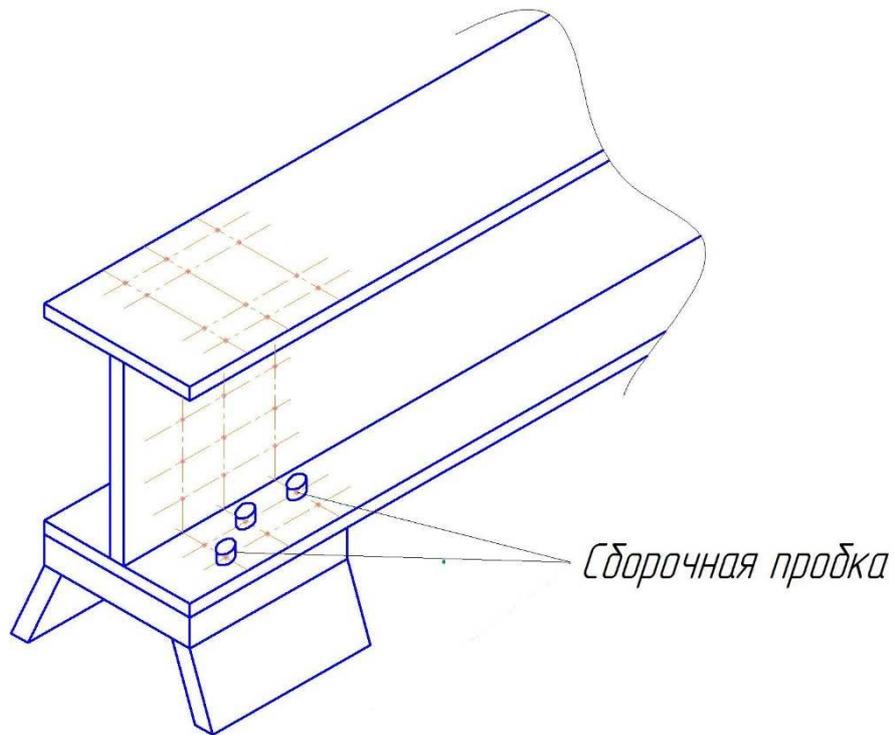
Установка колонны на кондуктор с помощью сборочных пробок
